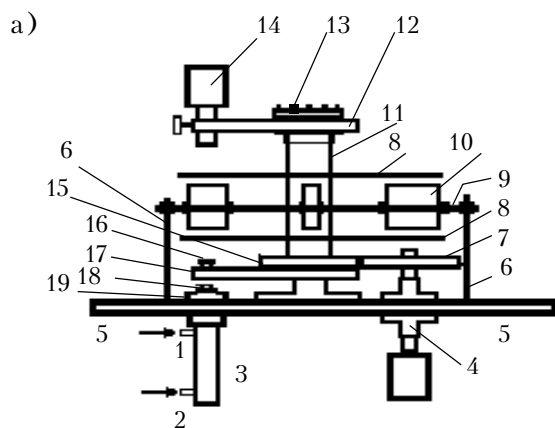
Установка диффузионной термокомпрессионной сварки
